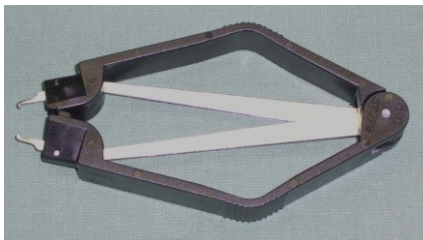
Ausziehwerkzeug für PLCC-Bausteine
